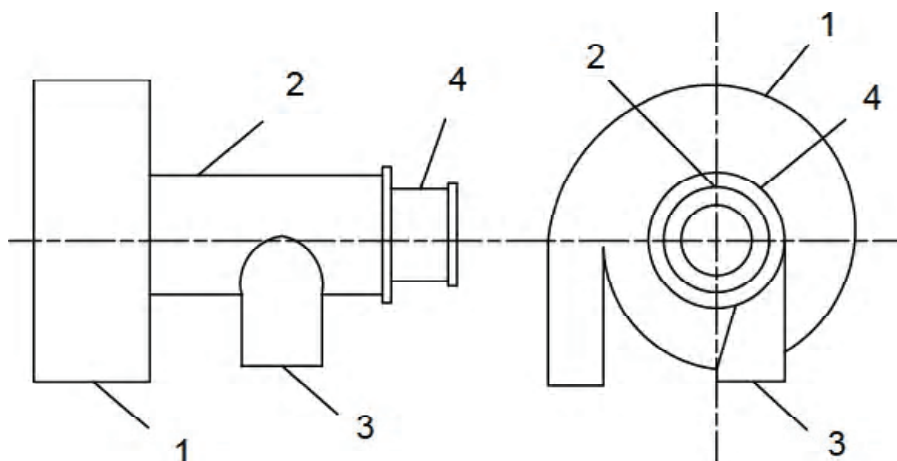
Схема пылеконцентратора: 1 – улиточный закручиватель; 2 – сепарационная камера; 3 – тангенциальный патрубок; 4 – аксиальный патрубок.
